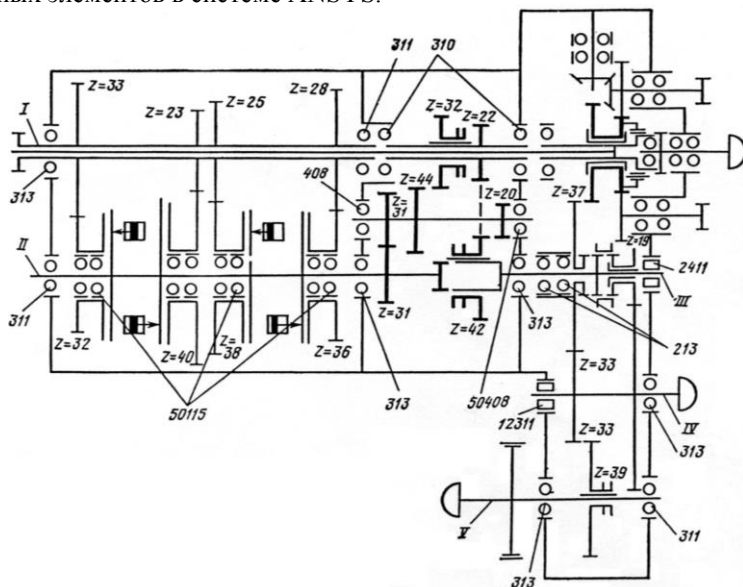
Кинематическая схема коробки передач и раздаточной коробки трактора Т-150К
